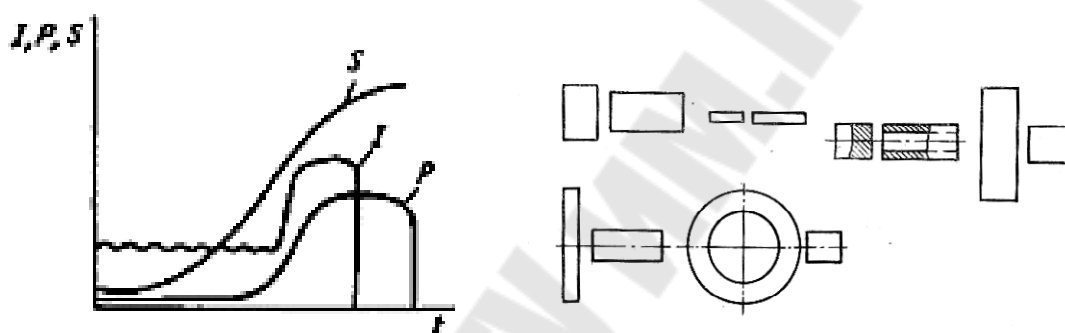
22. Циклограмма стыковой сварки оплавлением и виды сварных соединений
